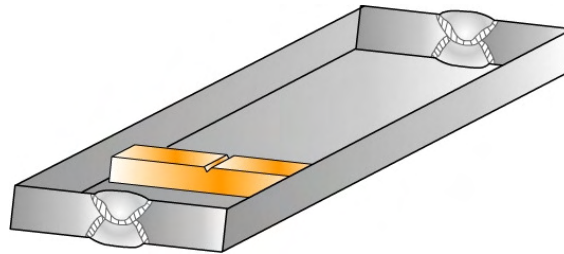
Representação esquemática da orientação de retiradas dos corpos-de-prova das juntas soldadas.
